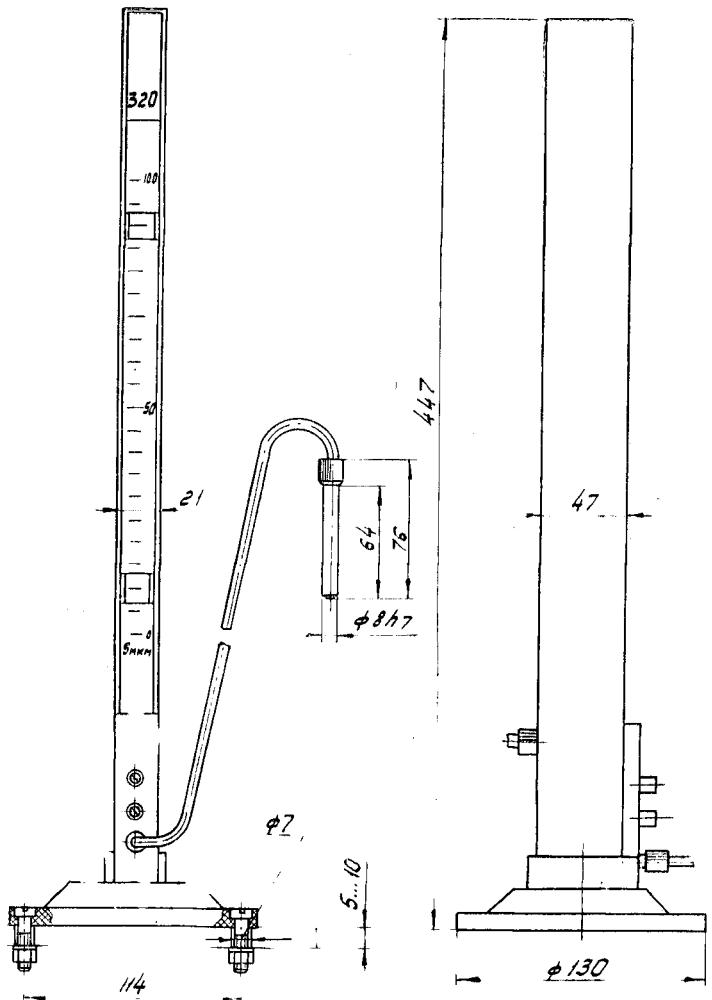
Габаритные и присоединительные размеры прибора (без блока фильтра со стабилизатором).
